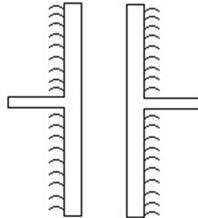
Esquema da soldadura no suporte da lança com $a=251\text{mm}$ e $b=250\text{mm}$
